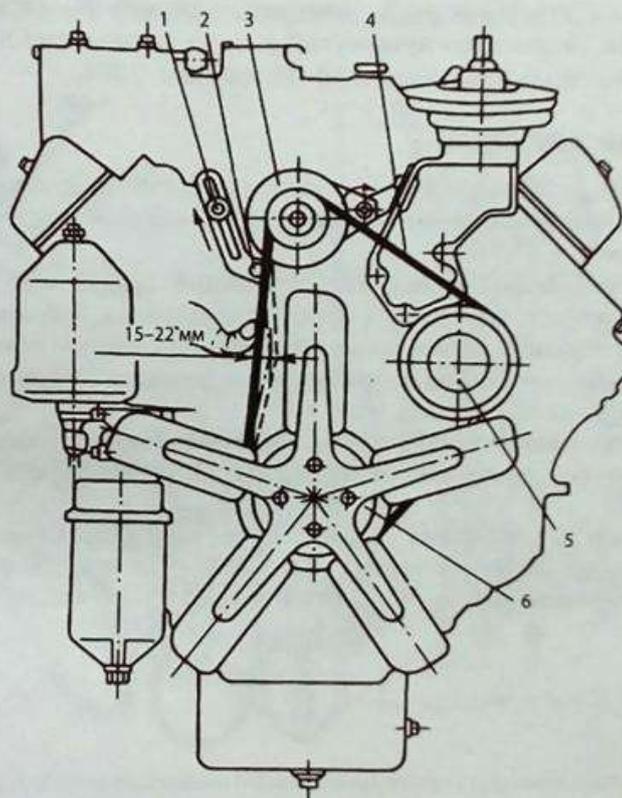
Перевірка і регулювання натягу паса вентилятора
